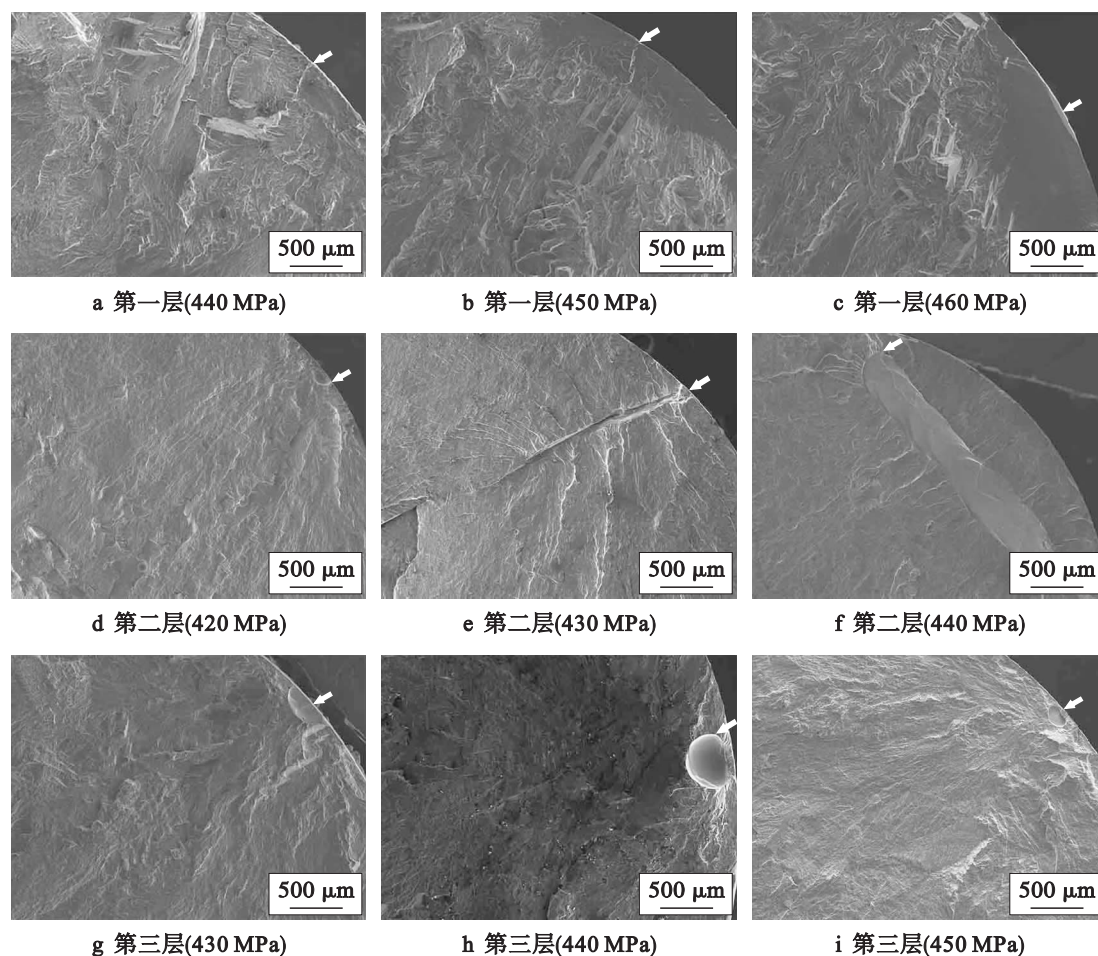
焊接接头在不同应力下的高周疲劳源区形貌
